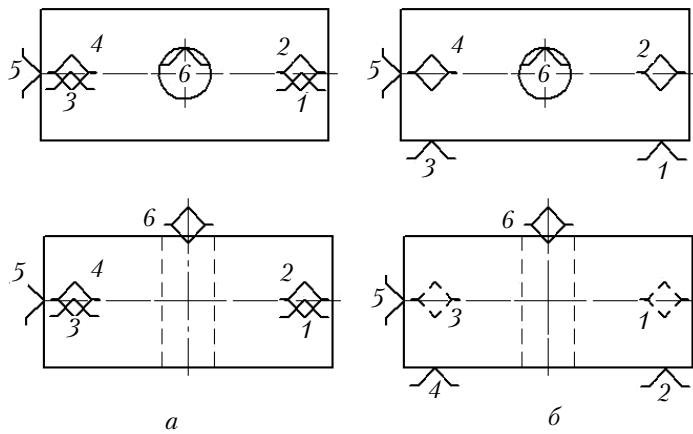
Теоретические схемы базирования заготовки по длинной цилиндрической поверхности и торцу:
